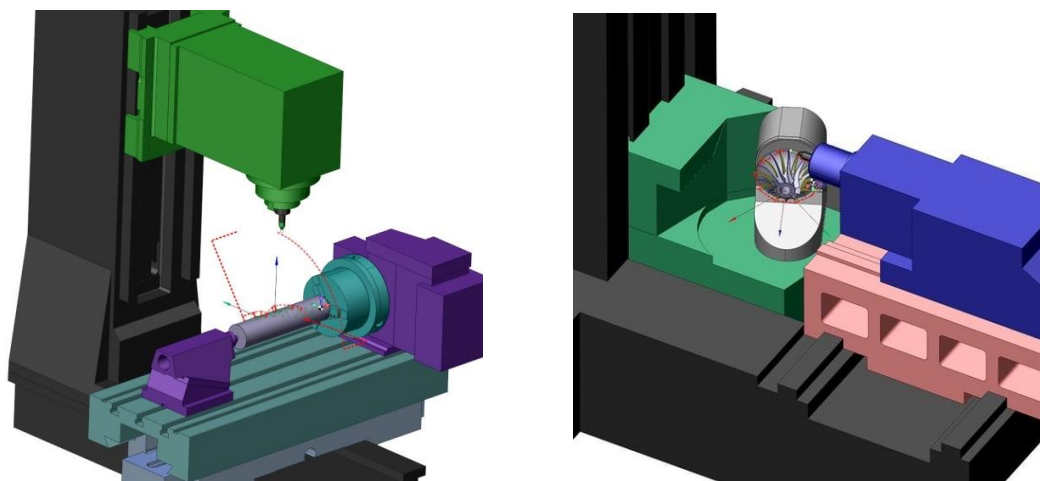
Схемы готовых компоновок станков в SprutCAM
